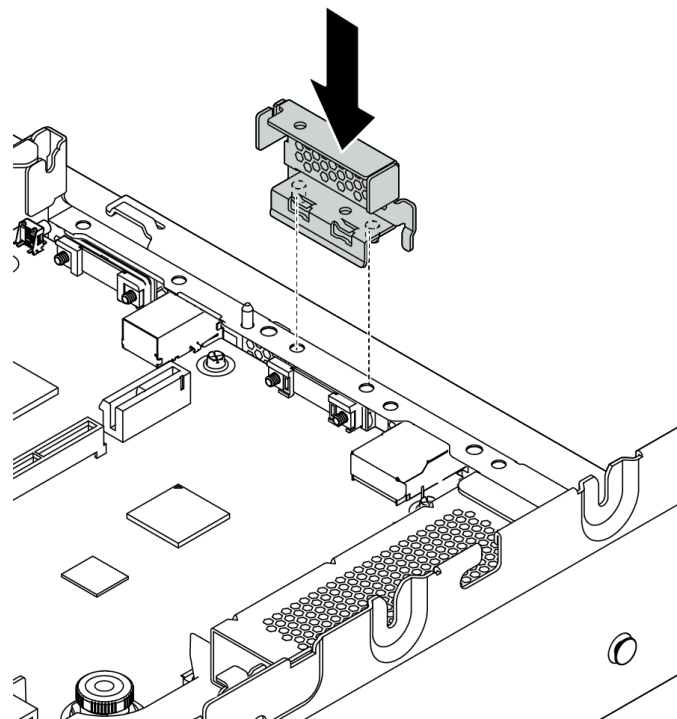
Installation du support mural arrière pour le boîtier d'unités arrière 3,5 pouces
